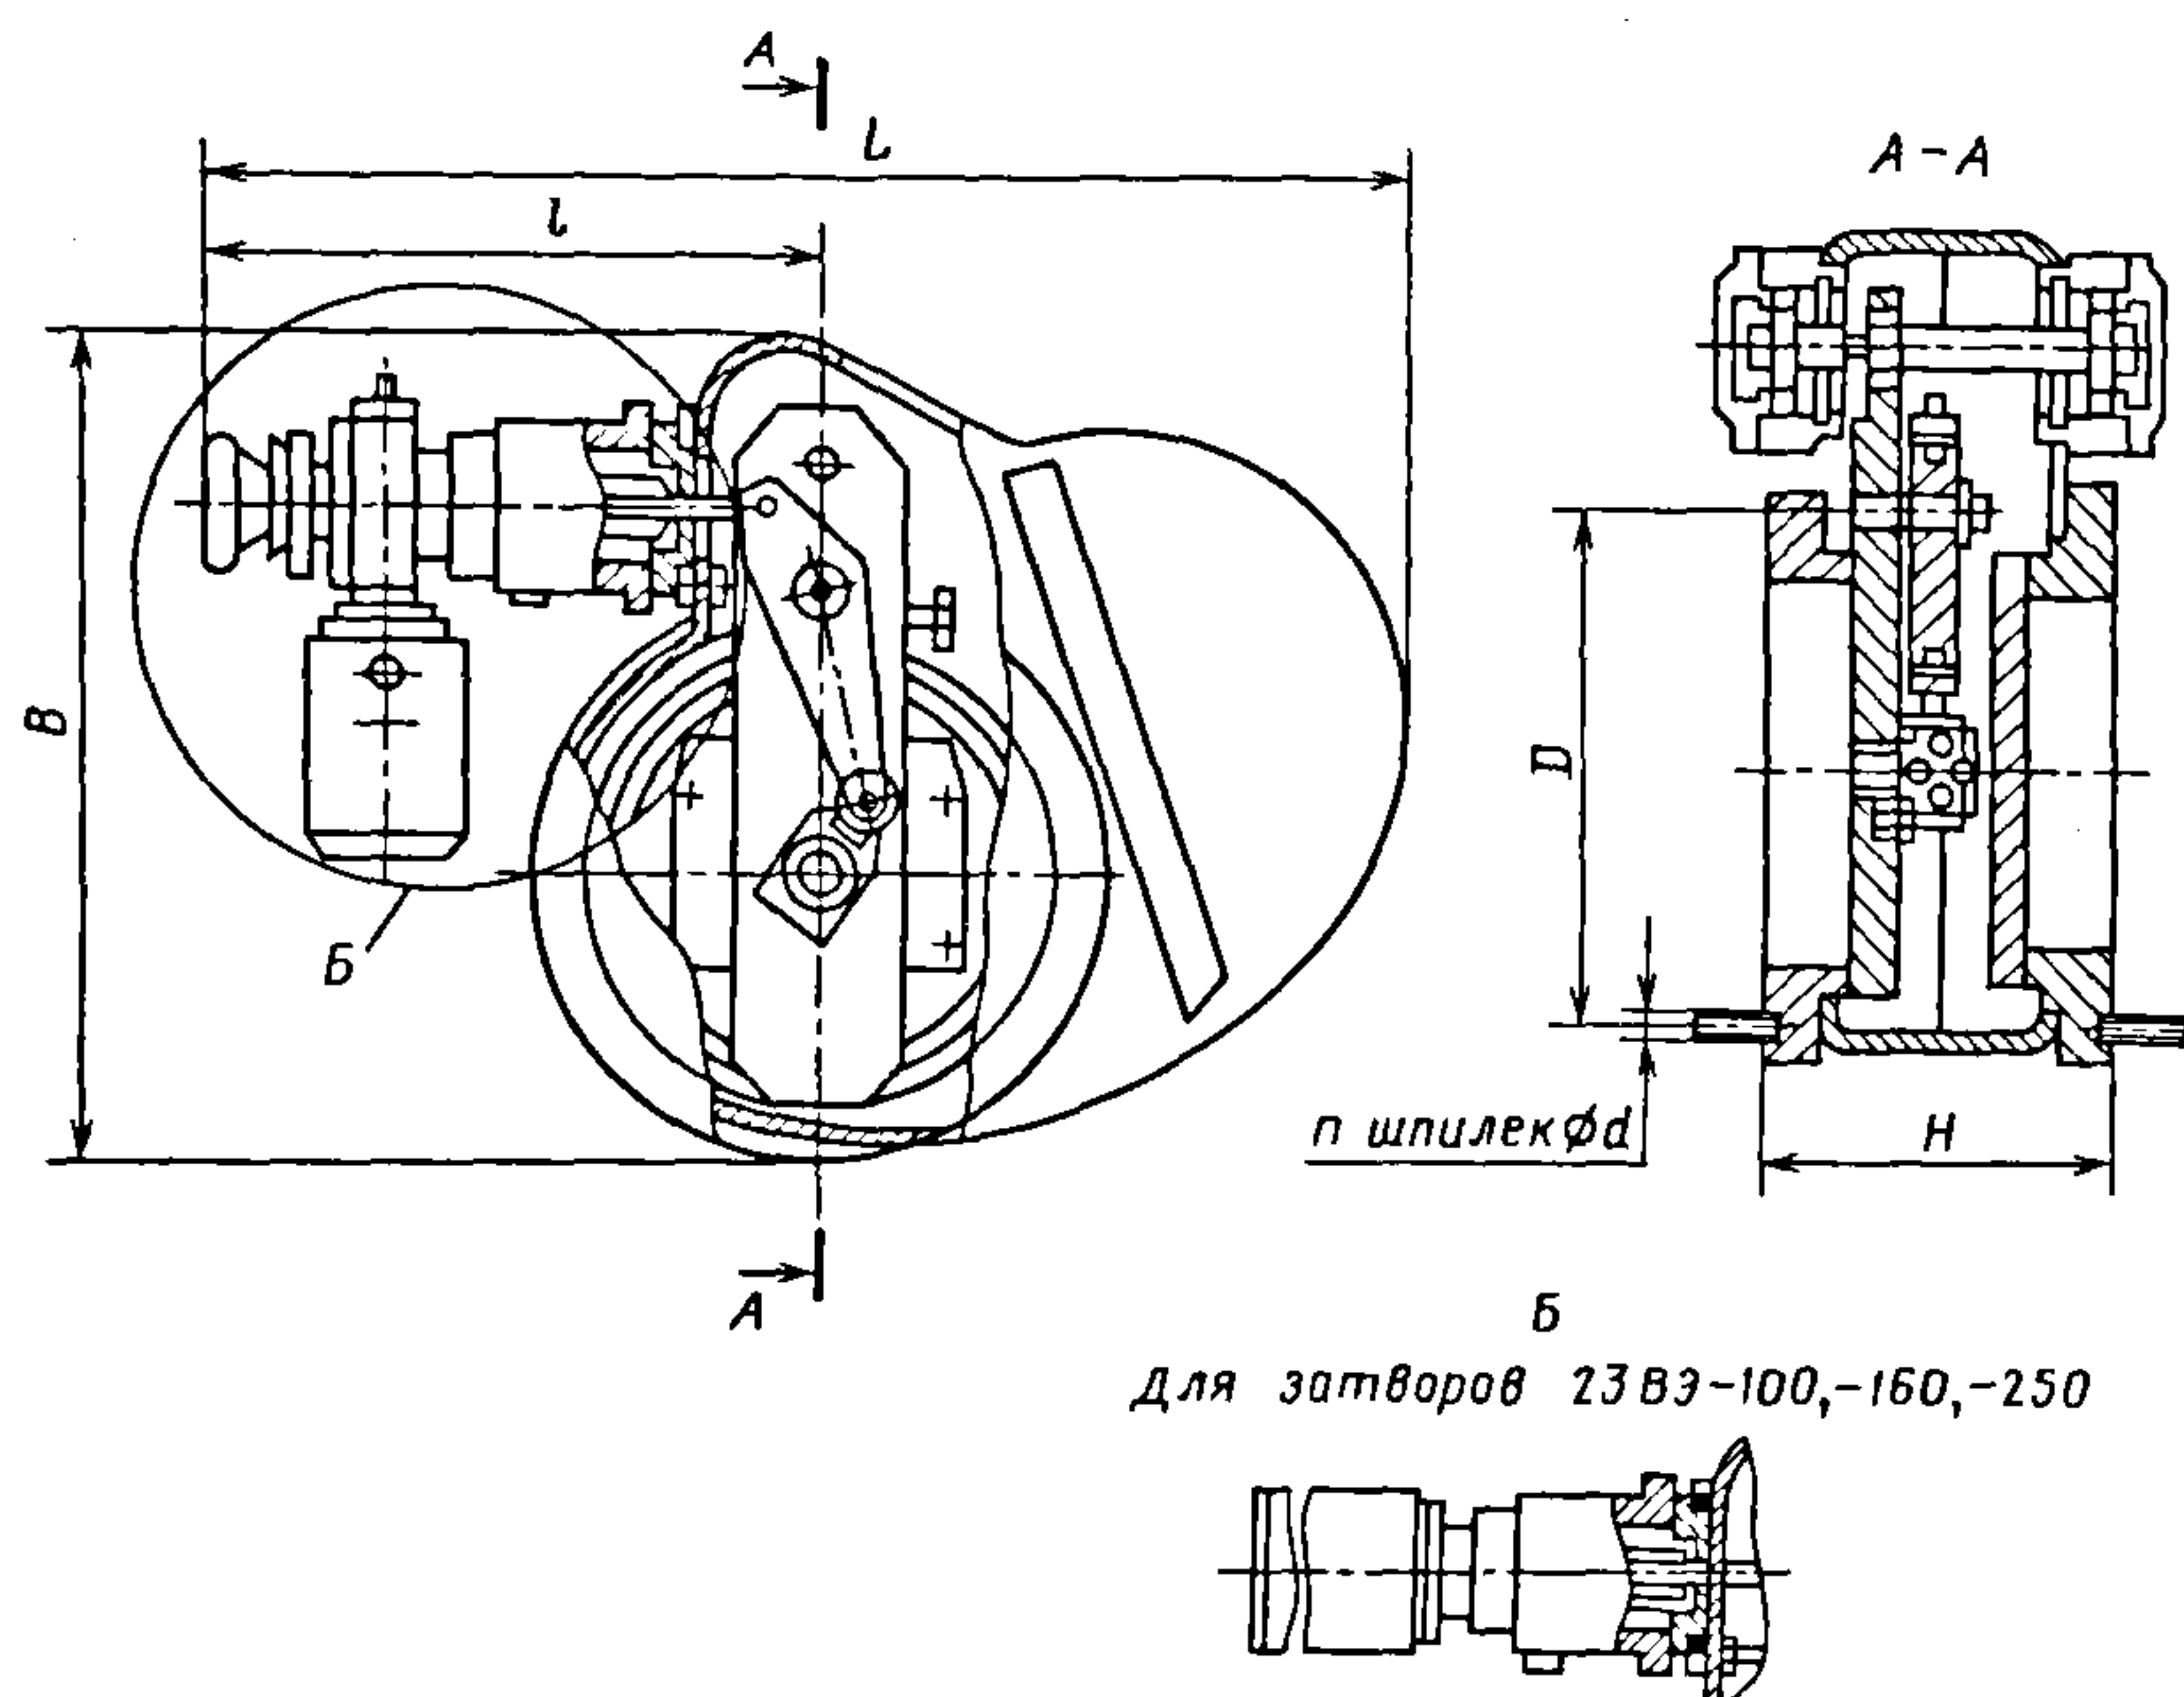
Габаритный чертеж вакуумных затворов типа 23ВЭ
